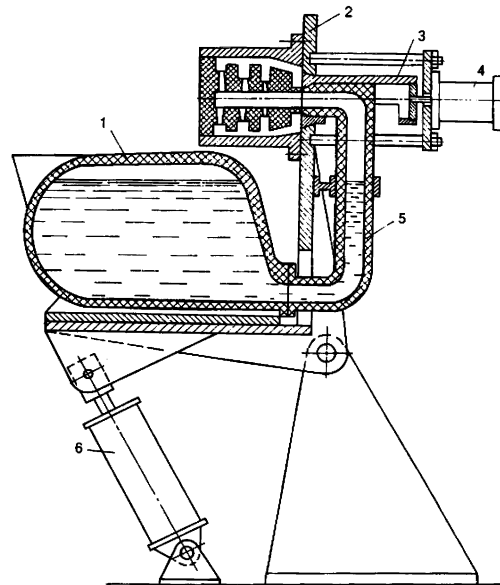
Принципиальная схема процесса: 1 – металлоприемник; 2 – плита для крепления форм; 3 – гильза для выталкивания отливки; 4 – пневмоцилиндр; 5 – металлопровод; 6 – механизм поворота
